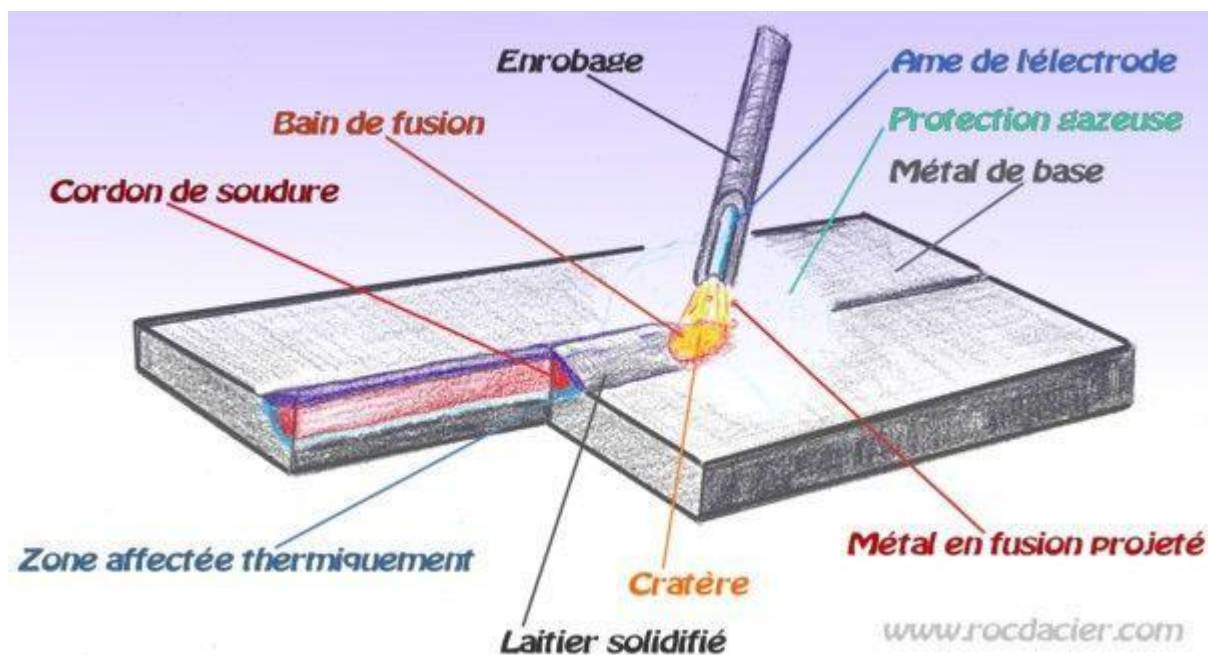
Procédé de soudage SMAW [4]
